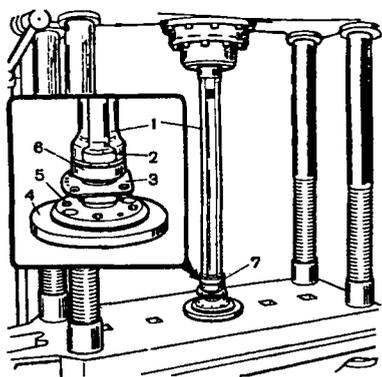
Запрессовка запорного кольца подшипника полуоси: 1 - оправка А.74107/2Р; 2 - запорное кольцо подшипника; 3 - пластина крепления подшипника и маслоотражатель в сборе с прокладкой; 4 - опорное кольцо А.74107/1Р; 5 - полуось; 6 - подшипник; 7 - обойма А.74107/4Р
